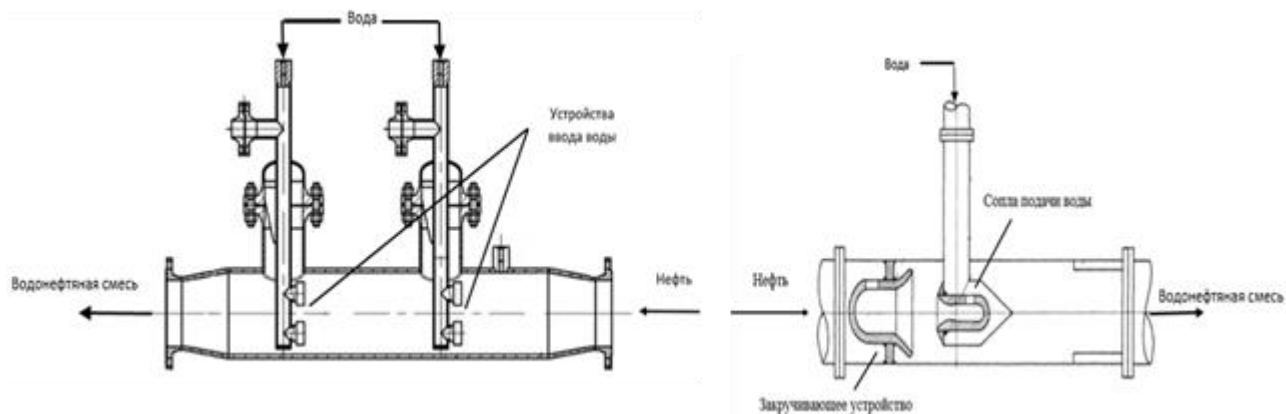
а) статический смеситель типа СНВ – 200, б) струйный гидродинамический смеситель
